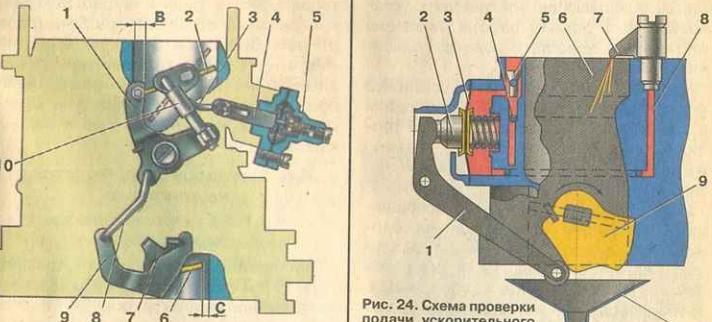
Схема регулировки пускового устройства: 1 - рычаг привода воздушной заслонки; 2 - воздушная заслонка; 3 - тяга пускового устройства; 4 - рейка пускового устройства; 5 - регулировочный винт; 6 - дроссельная заслонка первичной камеры; 7, 9 - рычаги; 8 - тяга привода; 10 - телескопическая тяга; В - пусковые заслонки заслонки
